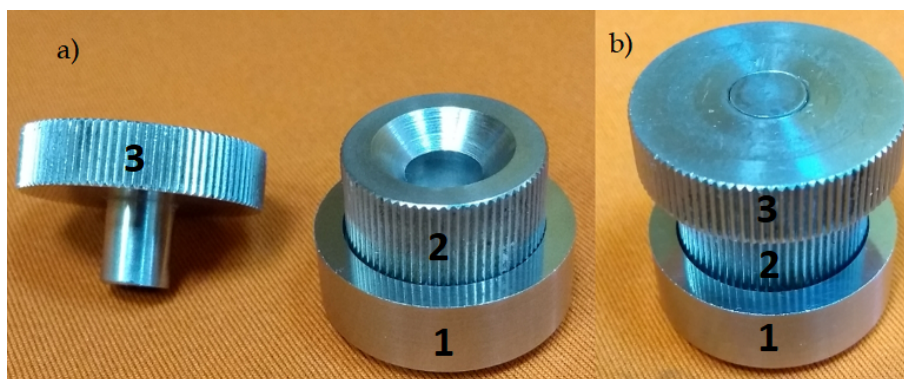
Posición en que deben colocarse los cilindros. a) Posición para rellenar. b) Posición para colocar en la prensa.
